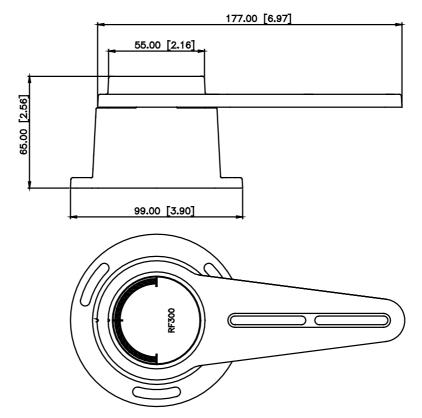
RF300 Ruder-Rückgeber - Abmessungen
